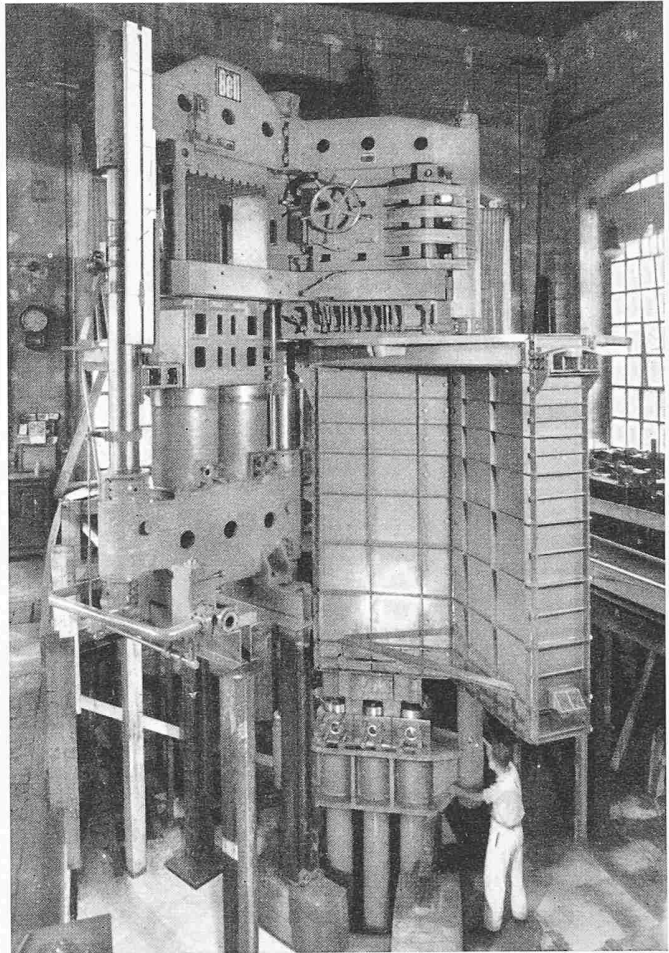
Werkstattmontage einer Ballenpresse von 1000 t Presskraft, Ballengewicht rd. 200 kg
